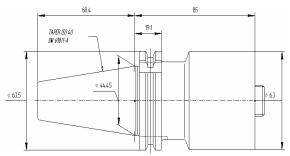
Базовый держатель C6-390.140-40 085
